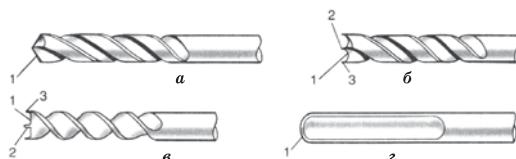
Сверла: а – спиральное; б – центровое, в – шнековое, г – ложечное (1 – режущая кромка; 2 – центр; 3 – подрезатель)
